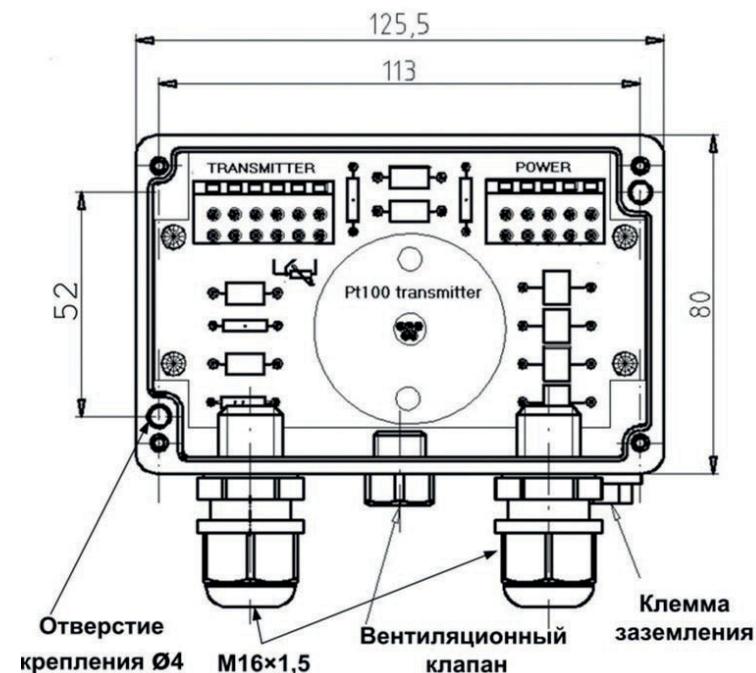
Внешний вид корпуса со снятой крышкой
